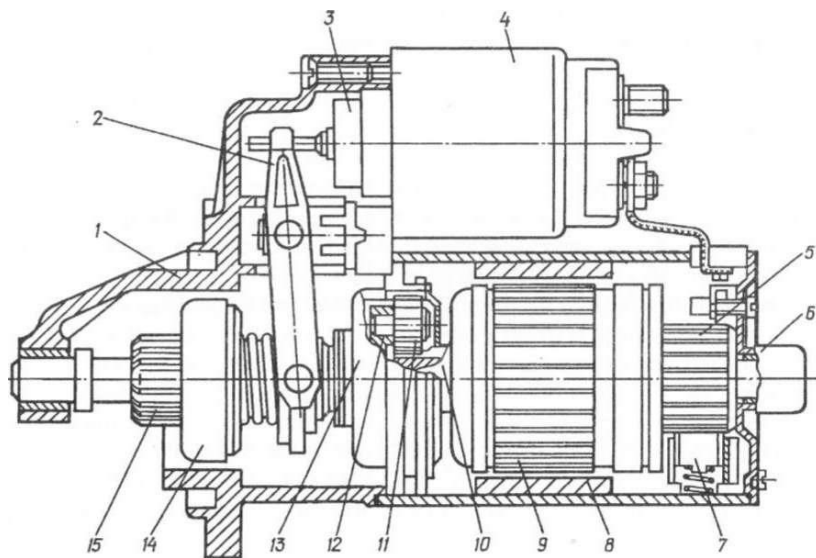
Конструкція стартера з планетарним редуктором і збудженням від постійних магнітів: 1 - передня кришка; 2 - приводний важіль; 3 - якір тягового реле; 4 - тягове реле; 5 - колектор електродвигуна; 6 - корпус підшипника; 7 - щітка; 8 - постійні магніти; 9 - якір; 10- первинний вал і ведуча шестірня редуктора; 11-зубчасте колесо-сателіт; 12 - водило; 13 - нерухоме
